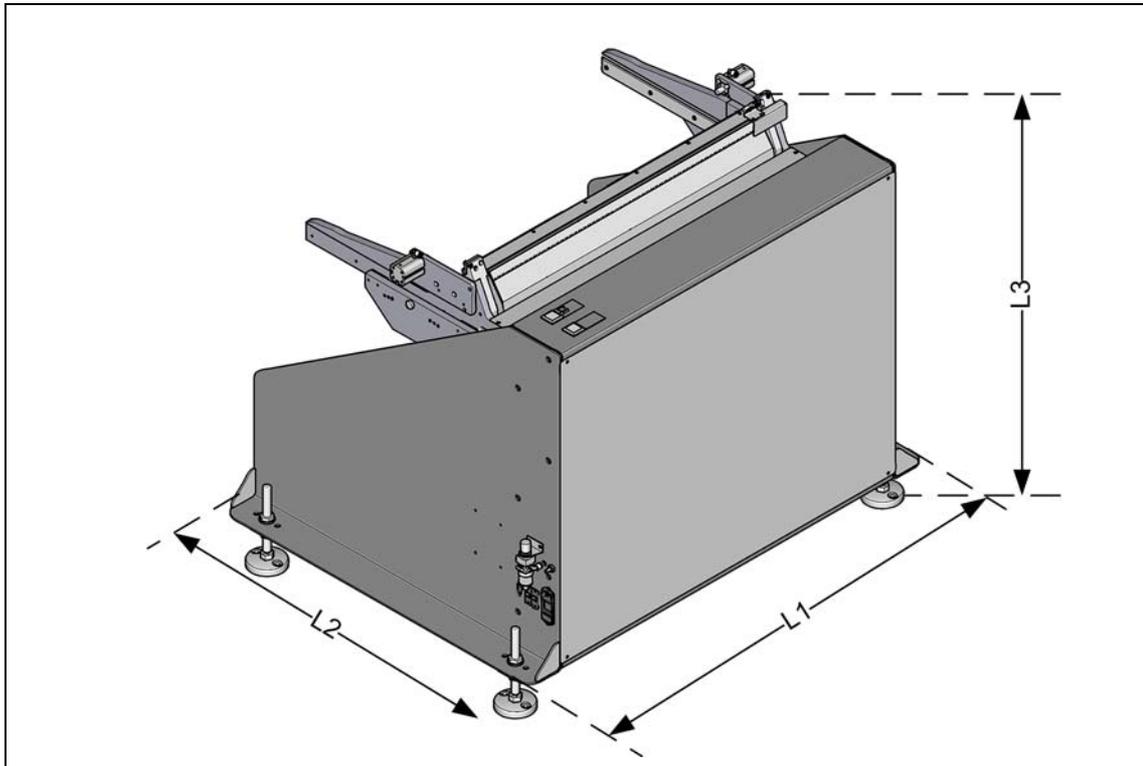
2 装卸站, SIPLACE SX- 系列 - 尺寸
